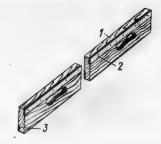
1— рейка; 2— пластина верхняя; 3— пластина нижняя
